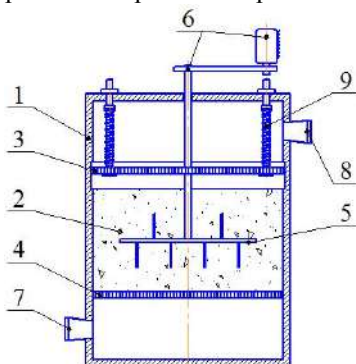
Адсорбер для зневоднення етанолу: 1 – корпус; 2 – сорбуючий шар (адсорбент); 3, 4 – обмежувальні решітки; 5 – розпушувач сорбенту; 6 – привід розпушувача; 7, 8 – патрубки; 9 – притиски
